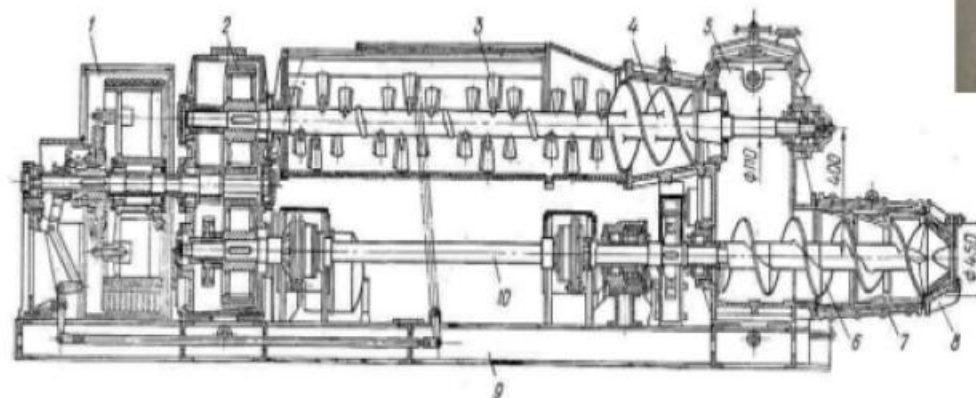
Ленточный вакуумный комбинированный пресс СМК-28 (СМ-443А):
